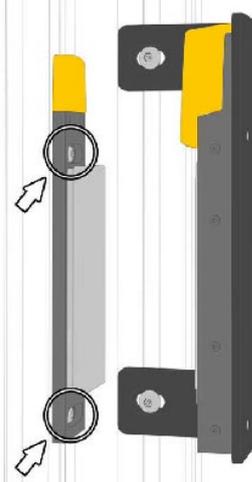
Ankerplatte am Profil der Schiebetüre anbringen, zur Prozesszuhaltung ausrichten und zur Prozesszuhaltung ausrichten. Schrauben M6 x 12 mm Torx festziehen.
